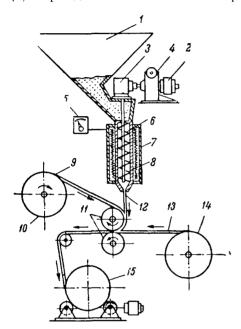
Схематическое изображение процесса сварки при помощи шприц-машины:
